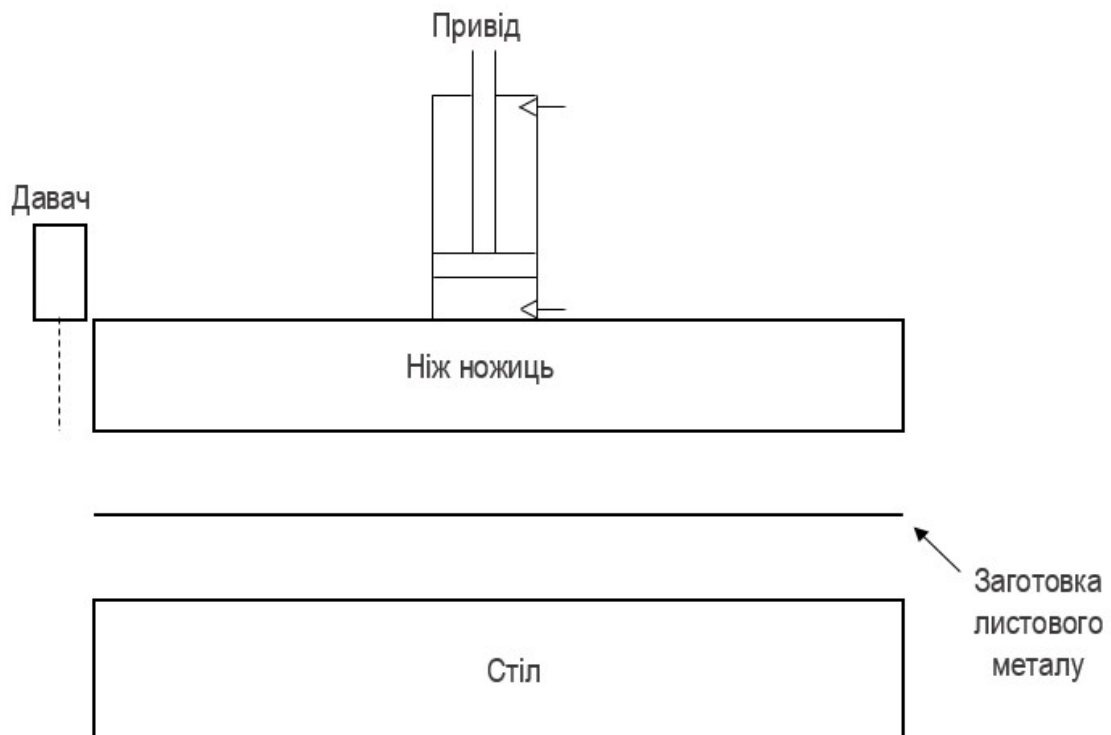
Ескіз типової лінії різання листового металу
